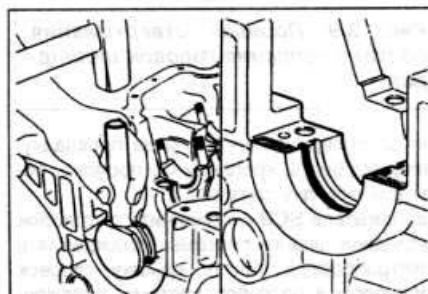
Запрессовка сальниковой набивки в опору заднего подшипника с помощью оправки 21.099
